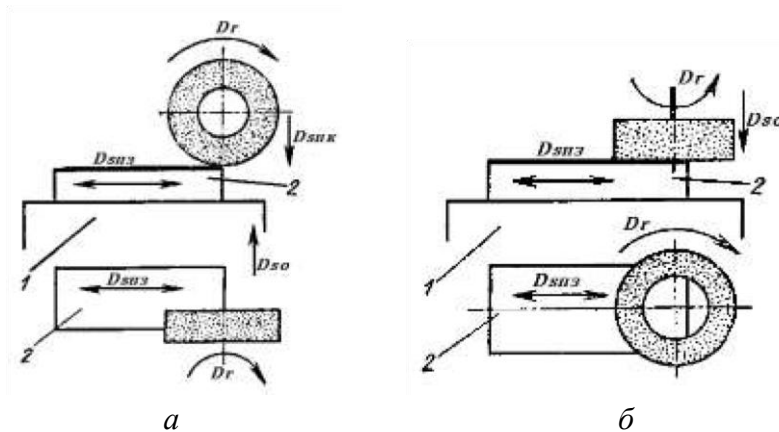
Схеми плоского шліфування. 1 – стіл; 2 – заготовка
